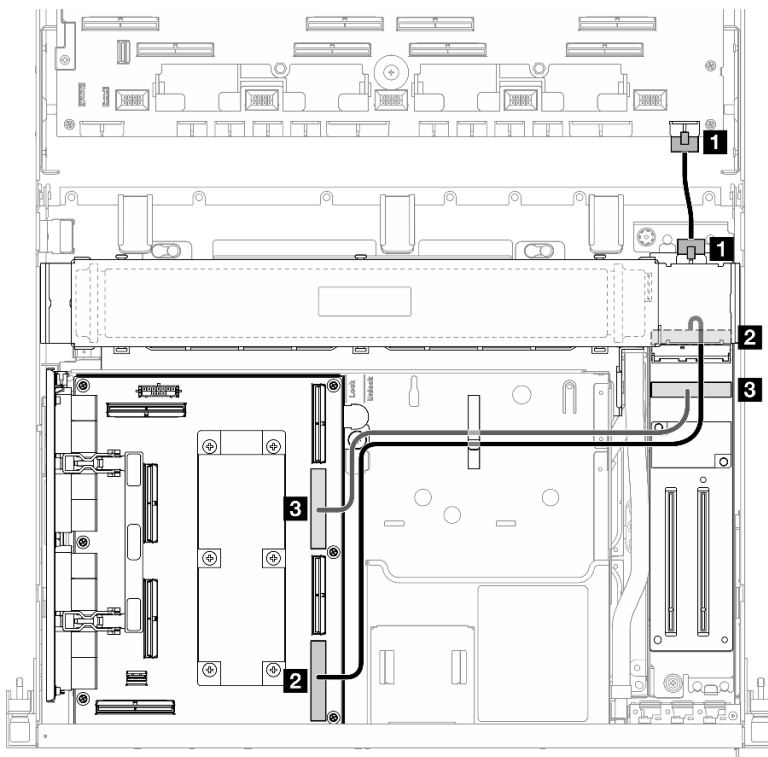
Disposición de los cables de la placa de expansión de E/S frontal
